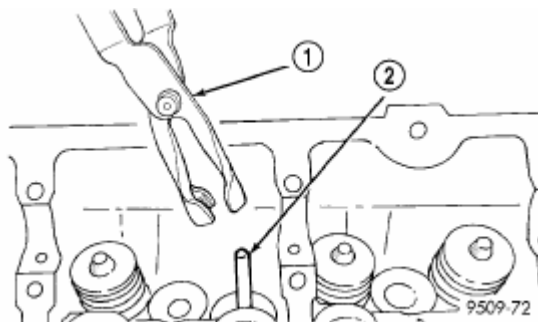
Приспособление для установки уплотнений стержня клапана.
